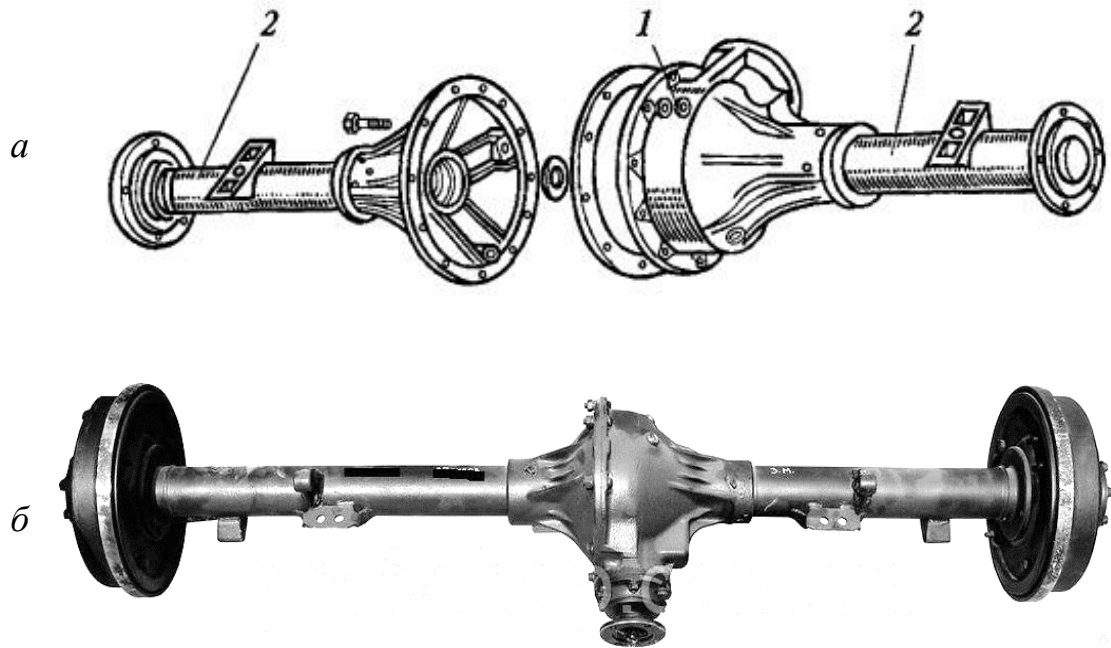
Ведучий міст з роз'ємним корпусом:
